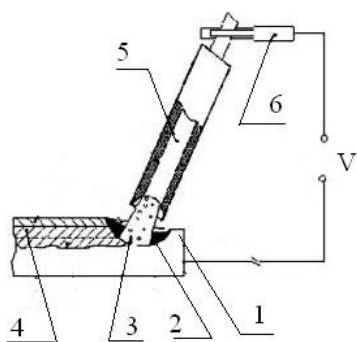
Схема ручной дуговой наплавки покрытым электродом: 1 – изделие; 2 – сварочная ванна; 3 – электрическая дуга; 4 – наплавленный валик; 5 – покрытый электрод; 6 – электрододержатель
